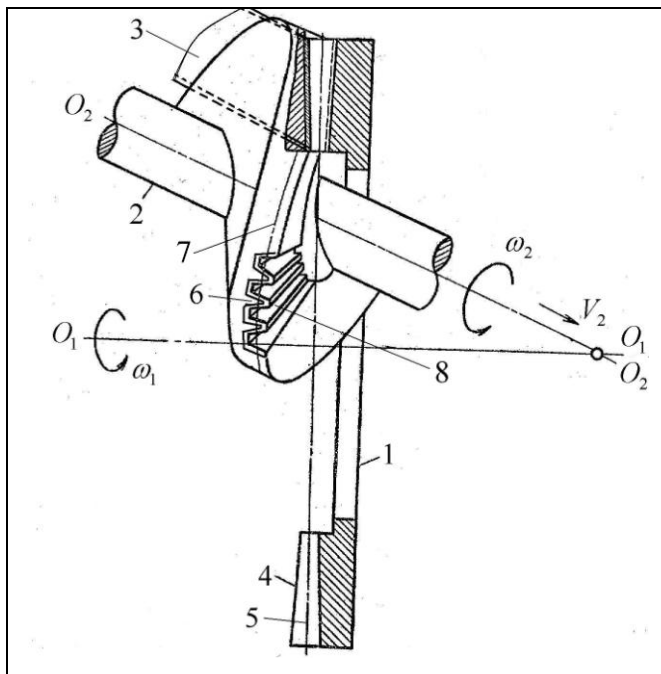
Пристрій для виготовлення гвинтових гофрованих заготовок.
